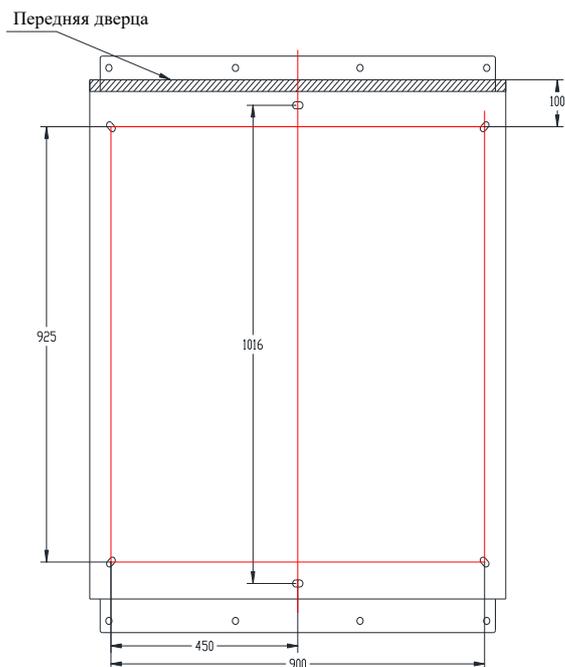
Установочный чертеж сейсмозащитных устройств с размерами
